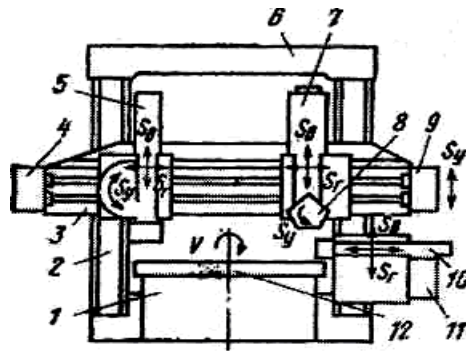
Двухстоечный токарно-карусельный станок.
